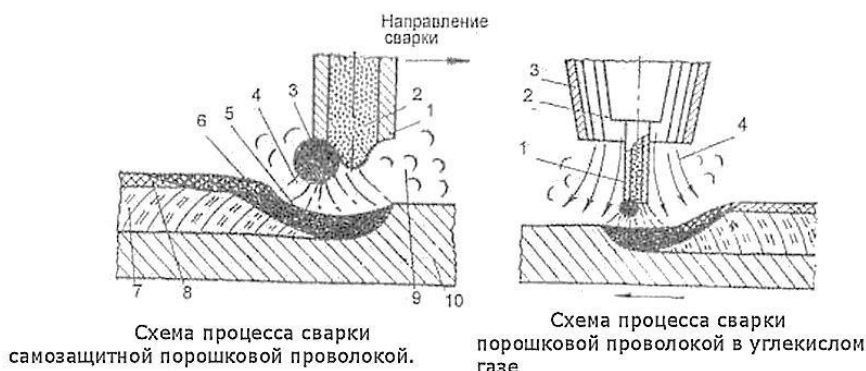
схема процесса сварки порошковой проволокой
